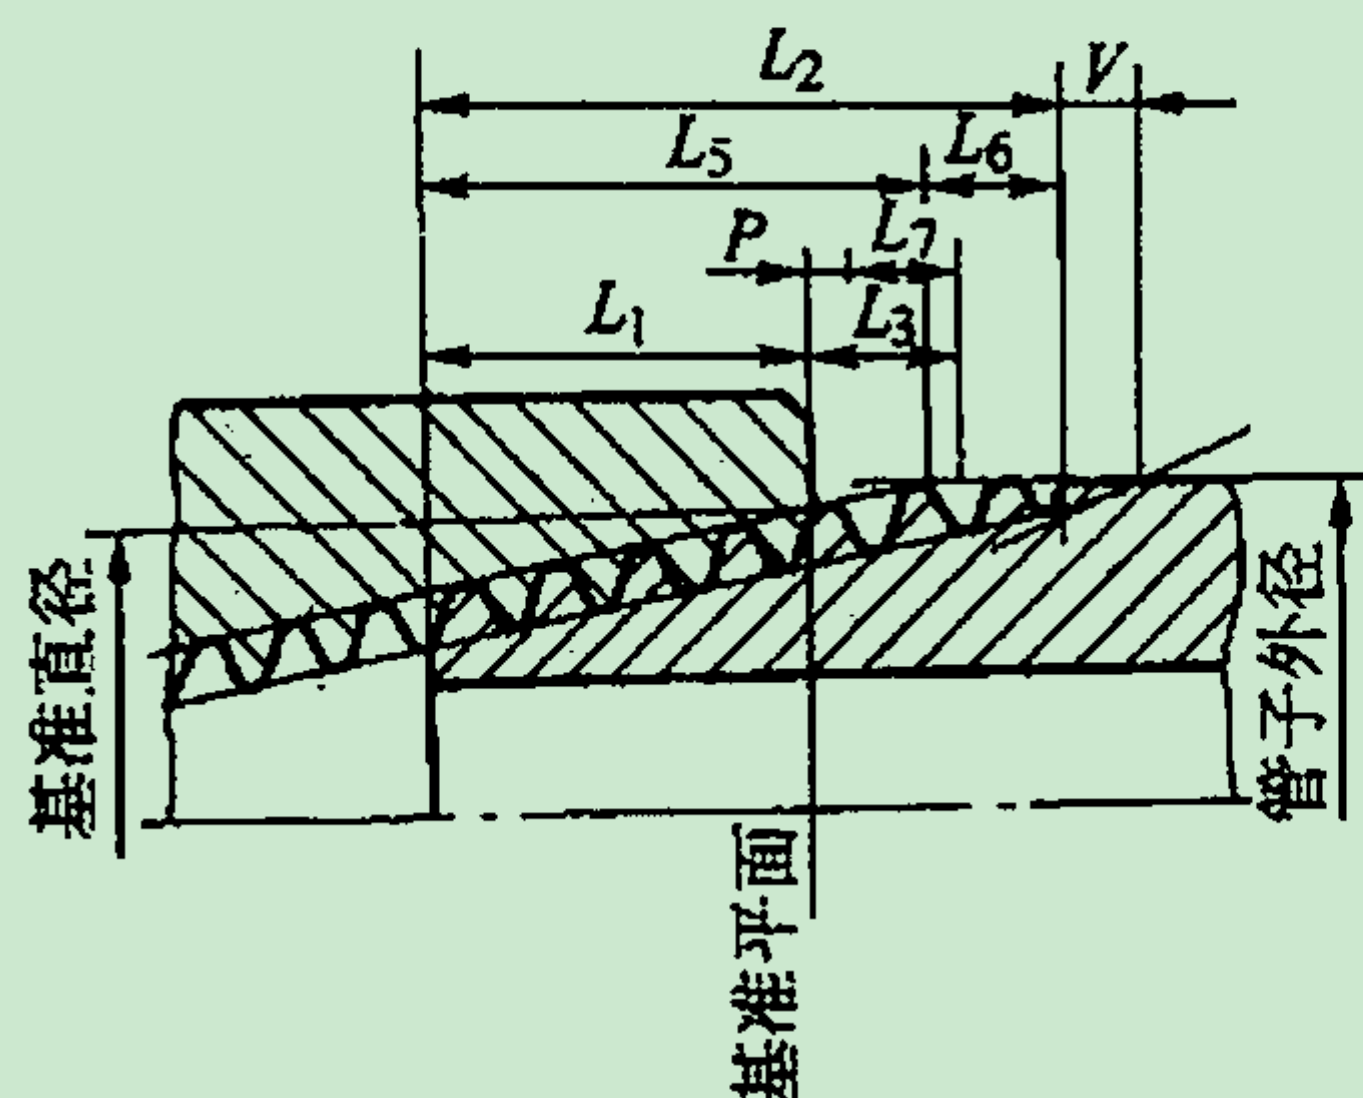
60°圆锥管螺纹的轴向尺寸
